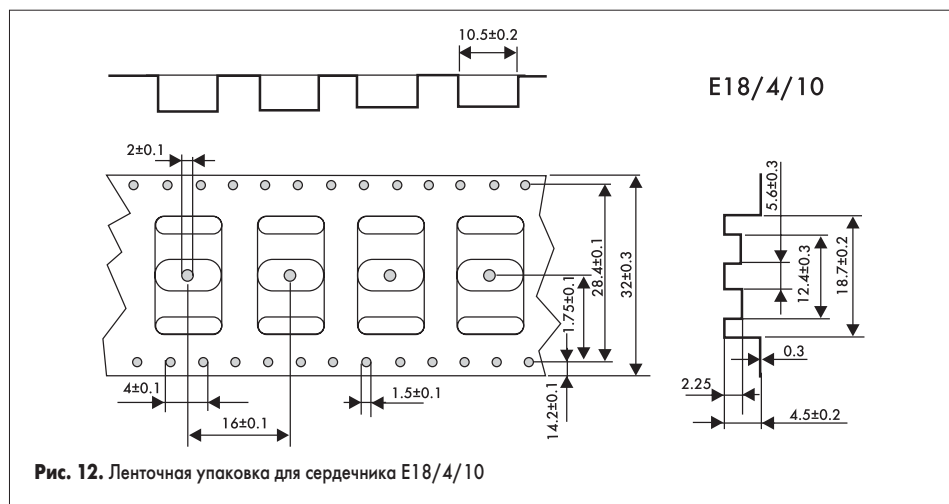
Ленточная упаковка для сердечника E18/4/10
